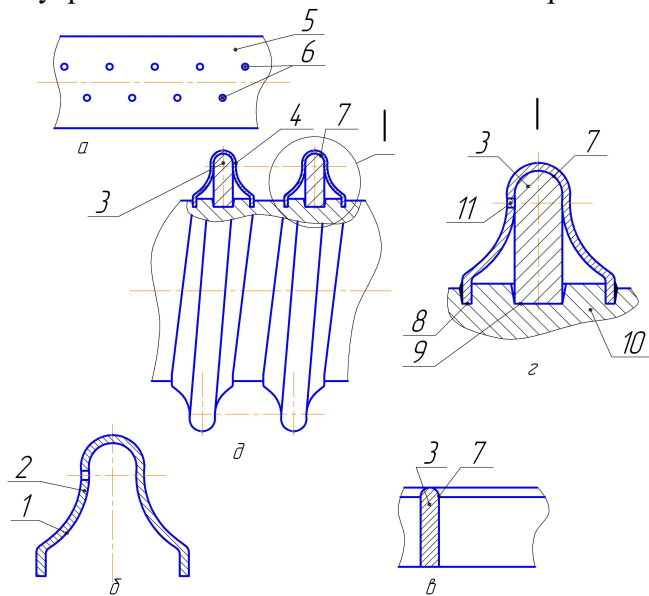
Гвинтові спіралі підвищеної міцності верстаті 16К20 або ДИП-200 чи ДИП-300 в залежності від розмірів спіралей і зусилля - формоутворення, зварювання деталей здійснюється в разі потреби зварювальною контактною машиною.
